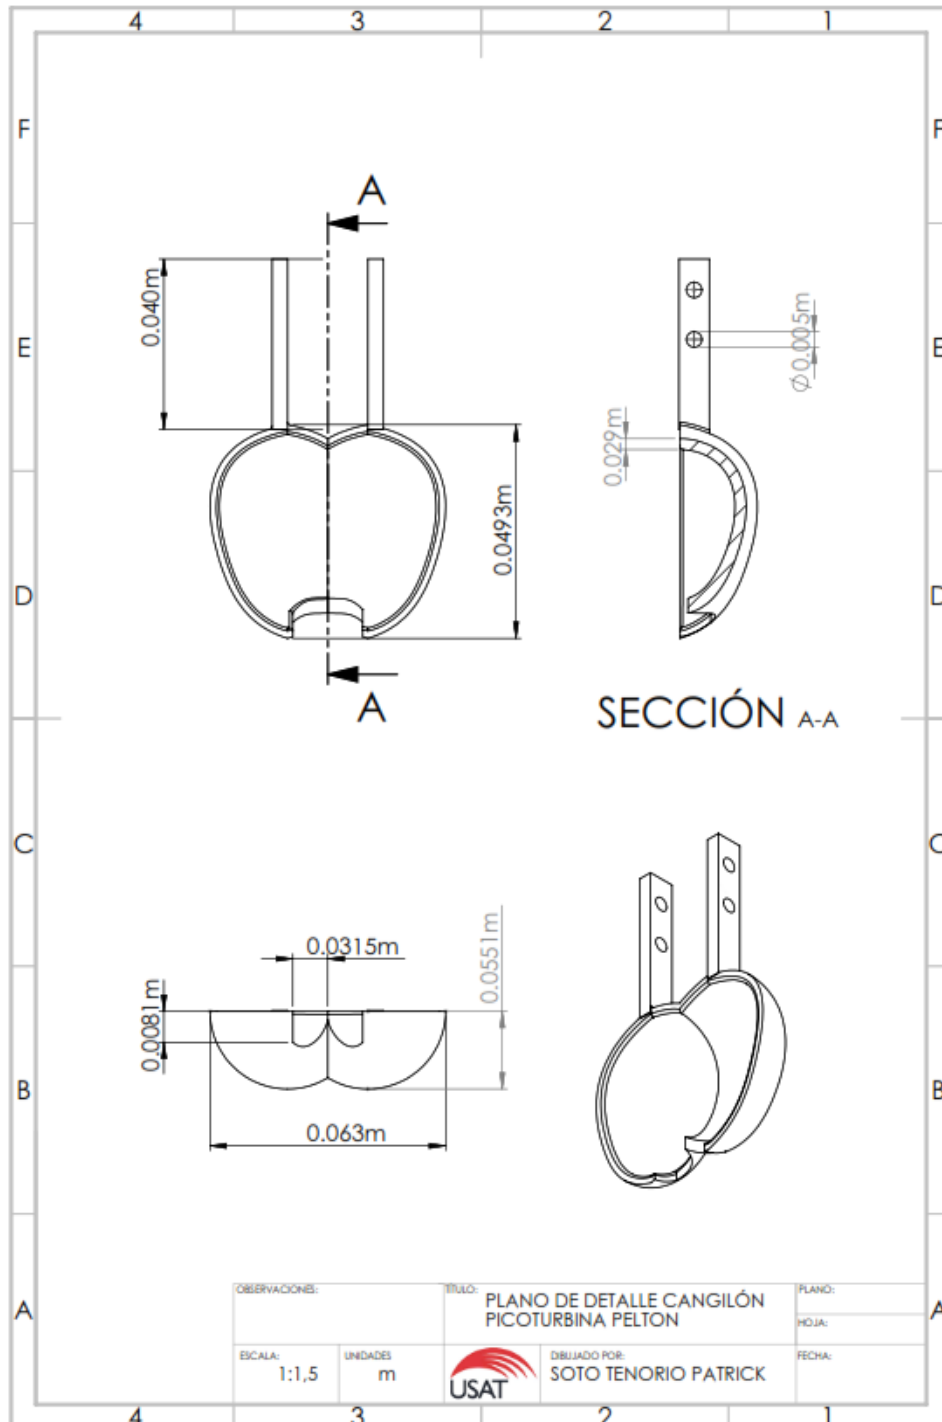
Plano de detalle cangilón picoturbina Pelton.
